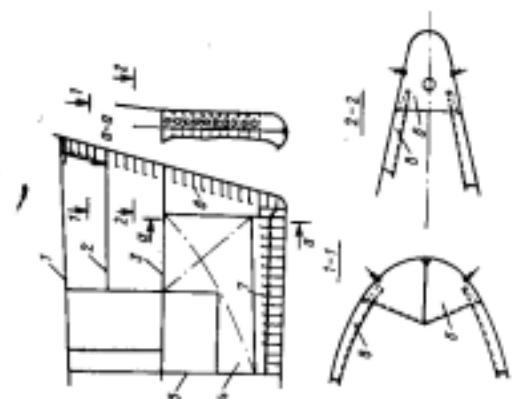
Схема конструкции форштевня с листовыми флангами на танкерах типа Т-2
